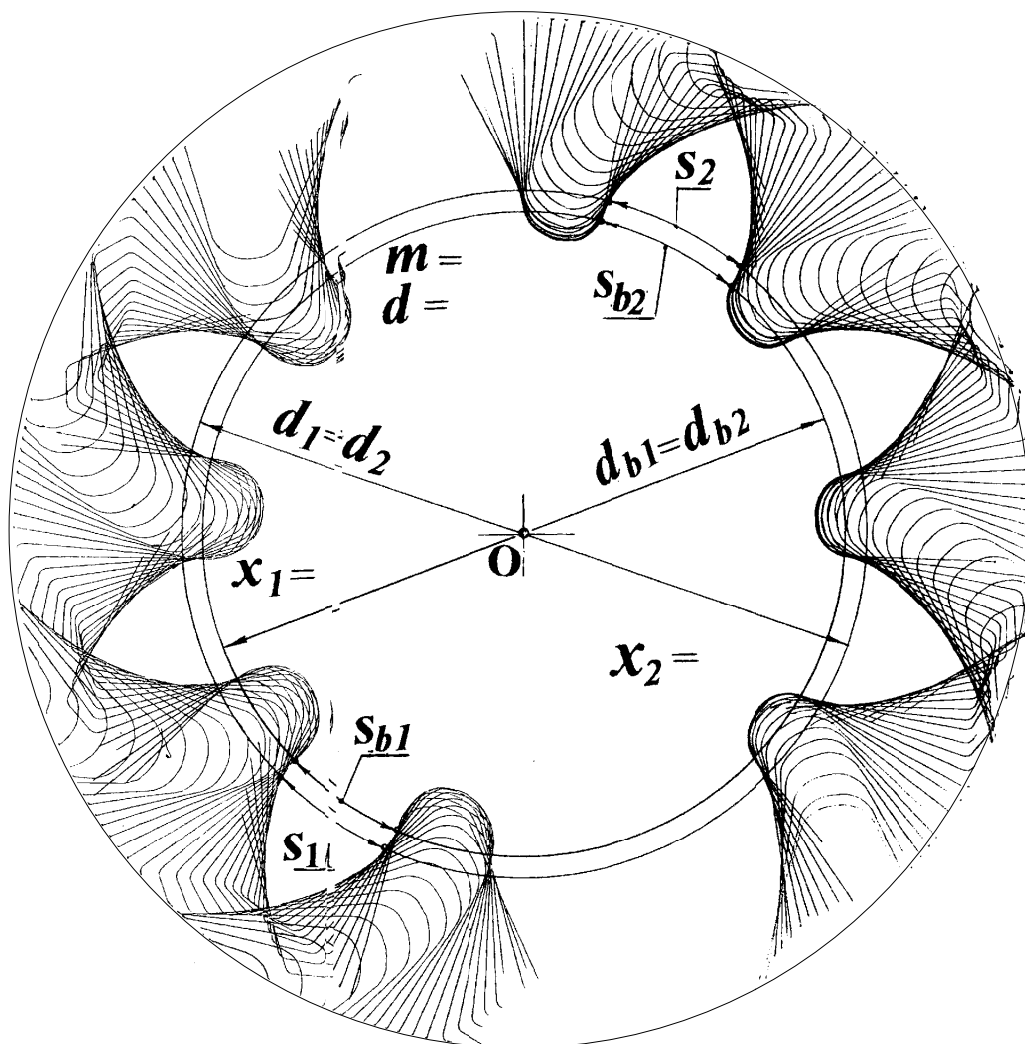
Пример оформления заготовки с нарезанными зубьями
